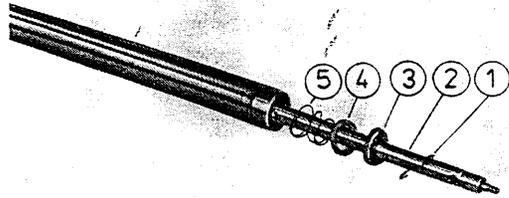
Déposer l'étrangleur, le disque de soupape et le ressort de compression
